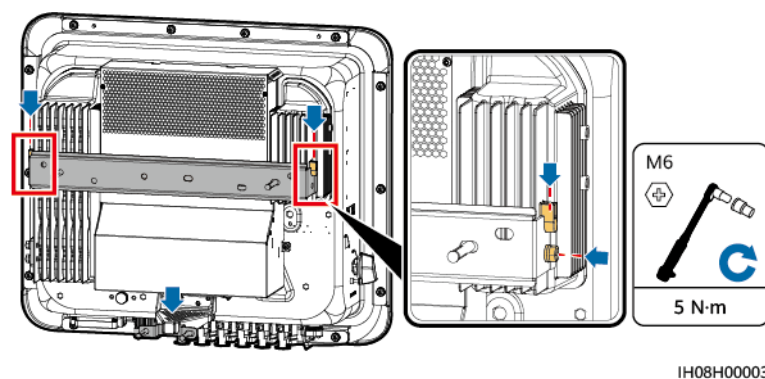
Installazione della vite di bloccaggio dell'interruttore CC
